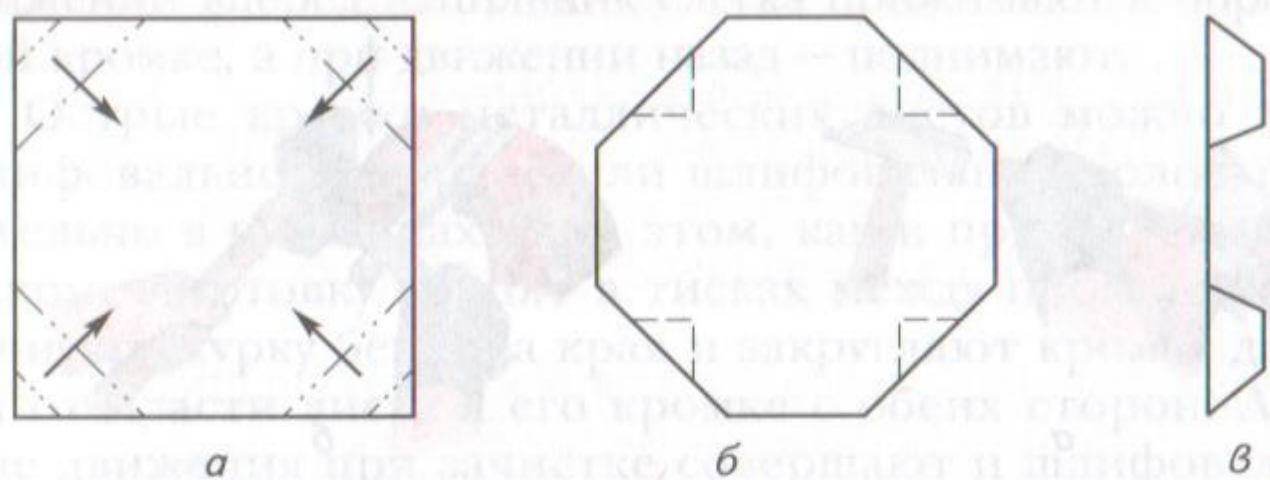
Подставка из жести: *а* — развёртка с размеченными линиями изгиба; изделие: *б* — главный вид; *в* — вид слева
